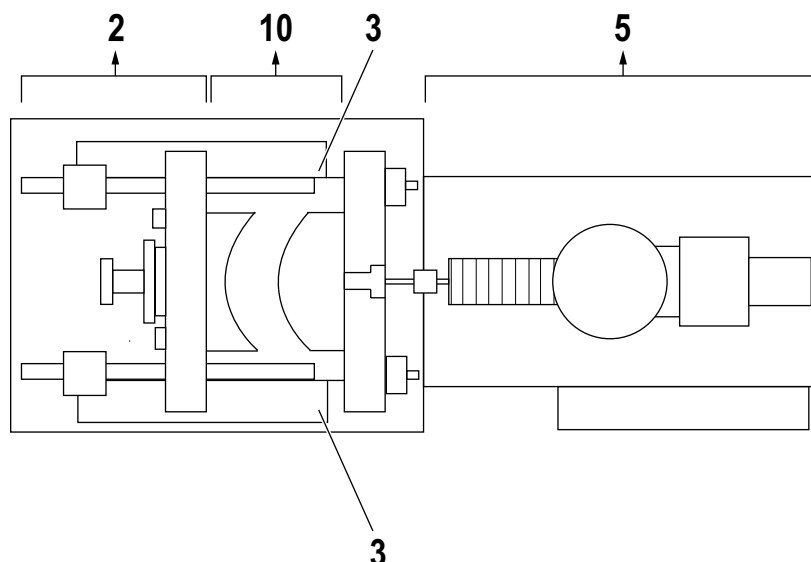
Zones de danger d'une machine de moulage par injection (vue de dessus)
